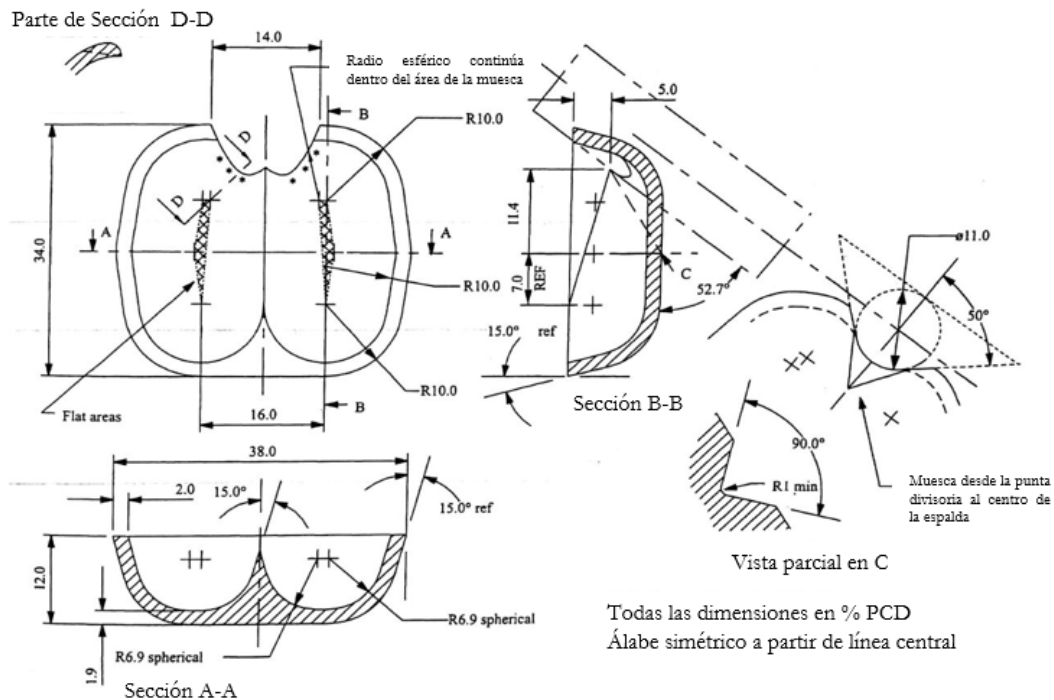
Dimensionamiento del álabe según el diámetro de paso PCD. Fuente: (Thake, 2000, pág. 33)
